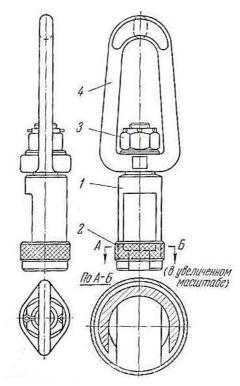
Элеватор для спуска и подъема бурильных труб: 1 – корпус; 2 – подвижное кольцо; 3 – зашплинтованная гайка; 4 – серьга
